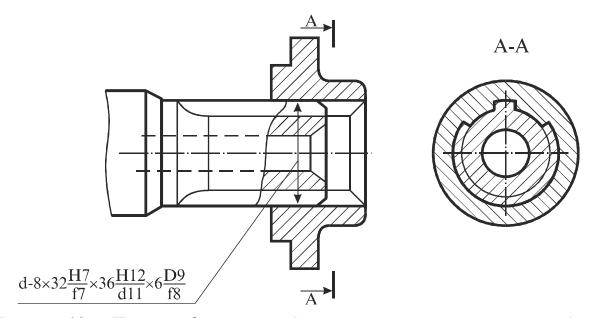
Пример оформления сборочного чертежа шлицевого соединения
